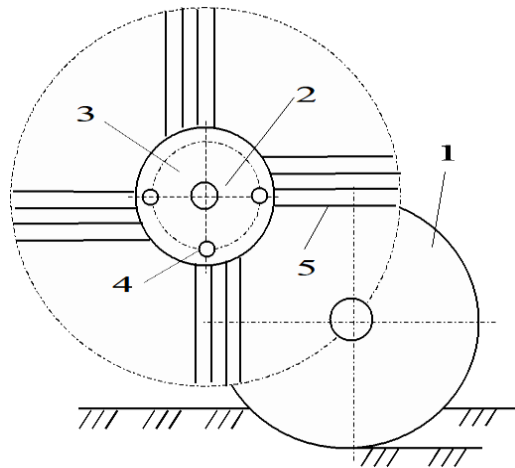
Конструктивна схема комбінованого викопуючого робочого: органу 1 - сферичний диск; 2 - очистний вал; 3 - барабан; 4 - вісь; 5 - лопать.
